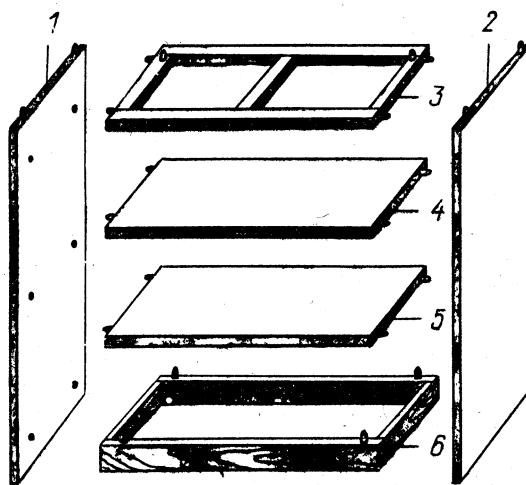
Детали разделочного стола-шкафа со вставными шипами: 1 и 2 — боковые стенки; 3 — подъяичная рамка; 4 — полка; 5 — днище; 6 — цоколь
